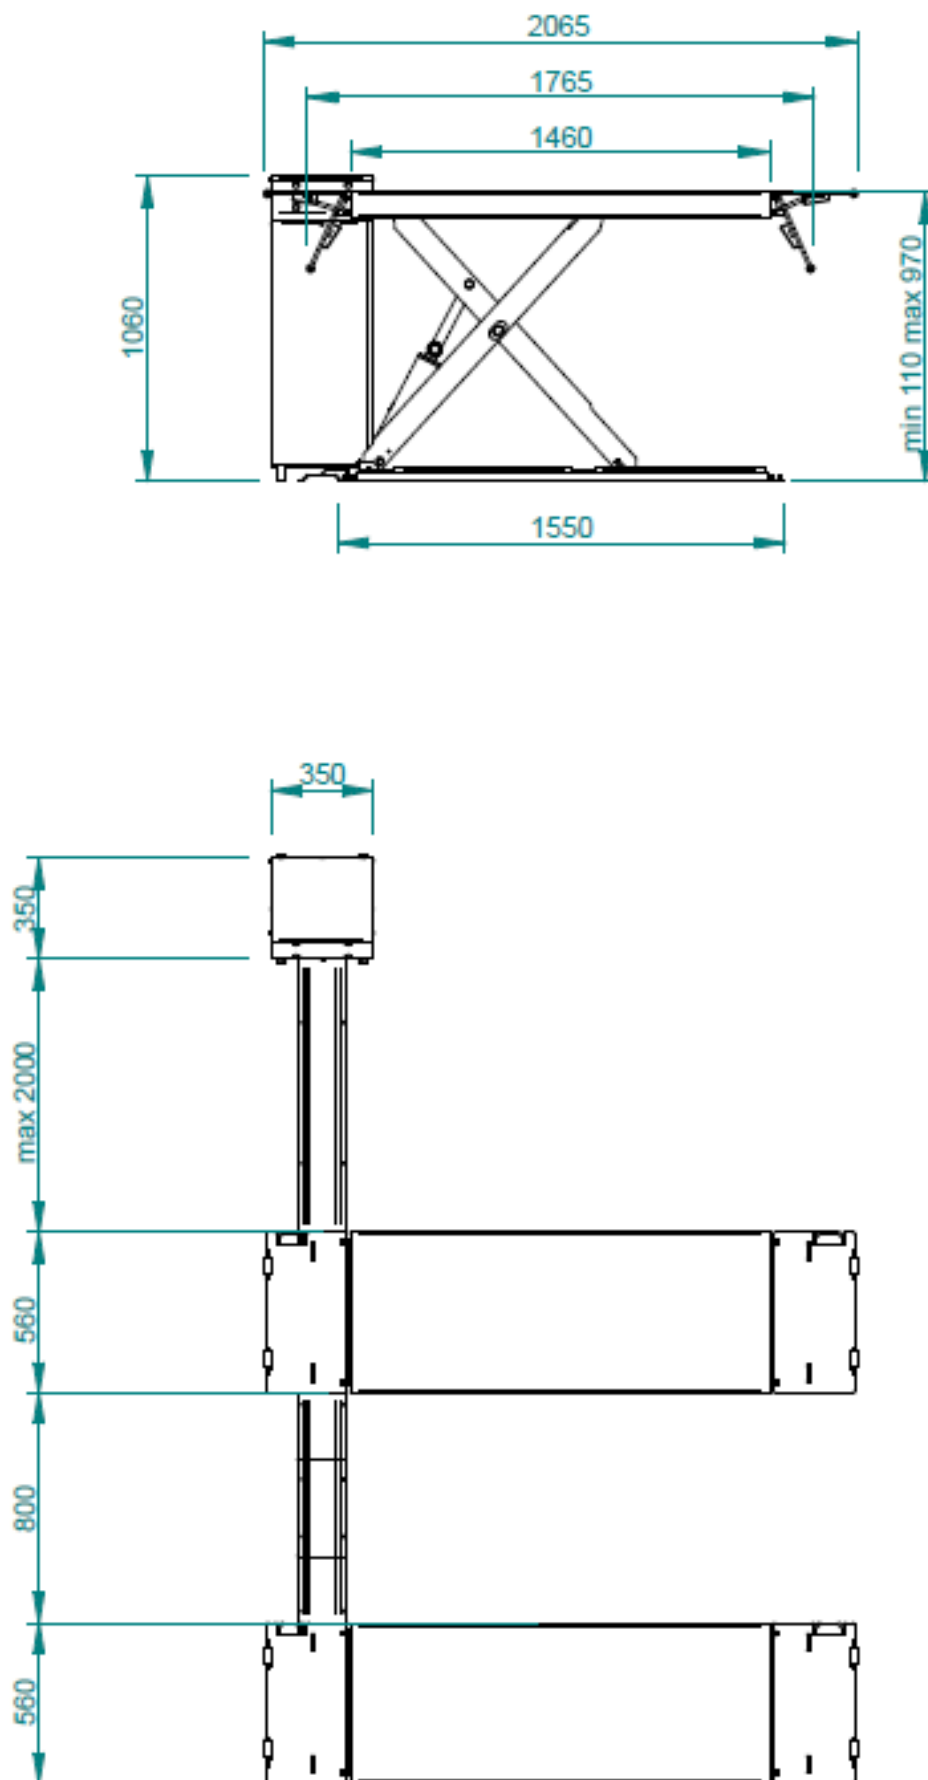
PLAN D'ENSEMBLE AVEC DES EXTENSIONS ET TRAVAUX CIVILS
